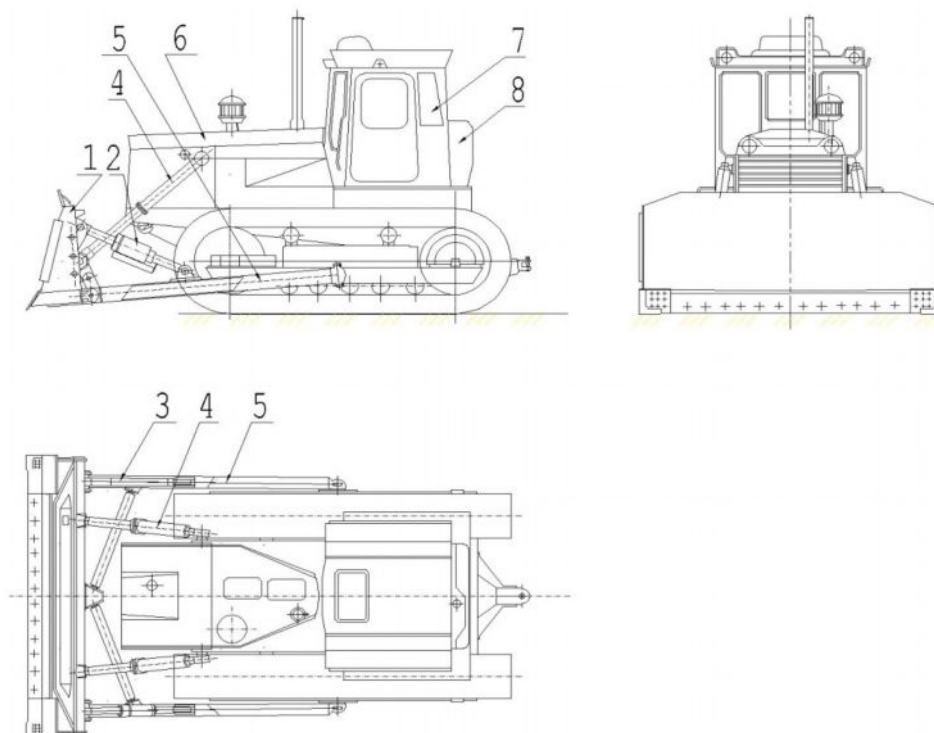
Конструктивная схема бульдозерного агрегата с модернизированным отвалом
